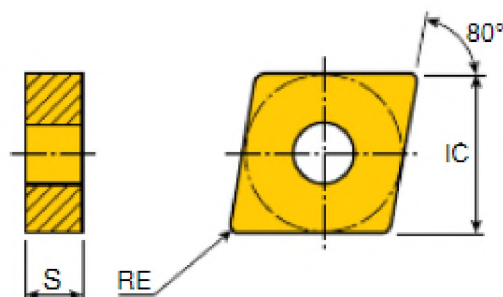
Пластина CNMG-090408EA .CVD покриття : TT5080
